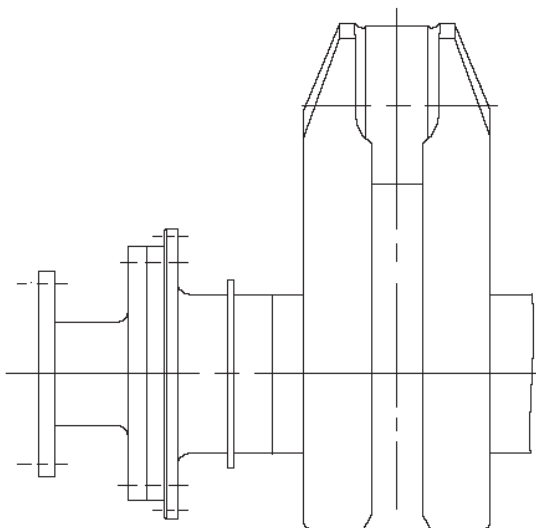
Конструкція зібраного колінчастий вал
